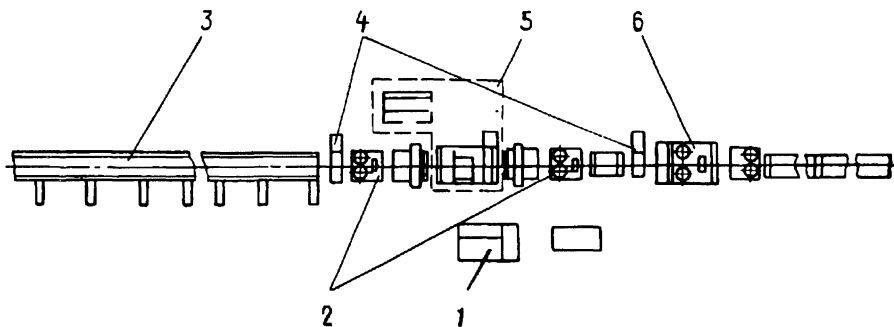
Линия К819 для контактной стыковой сварки и мерной резки стержневой арматуры:
